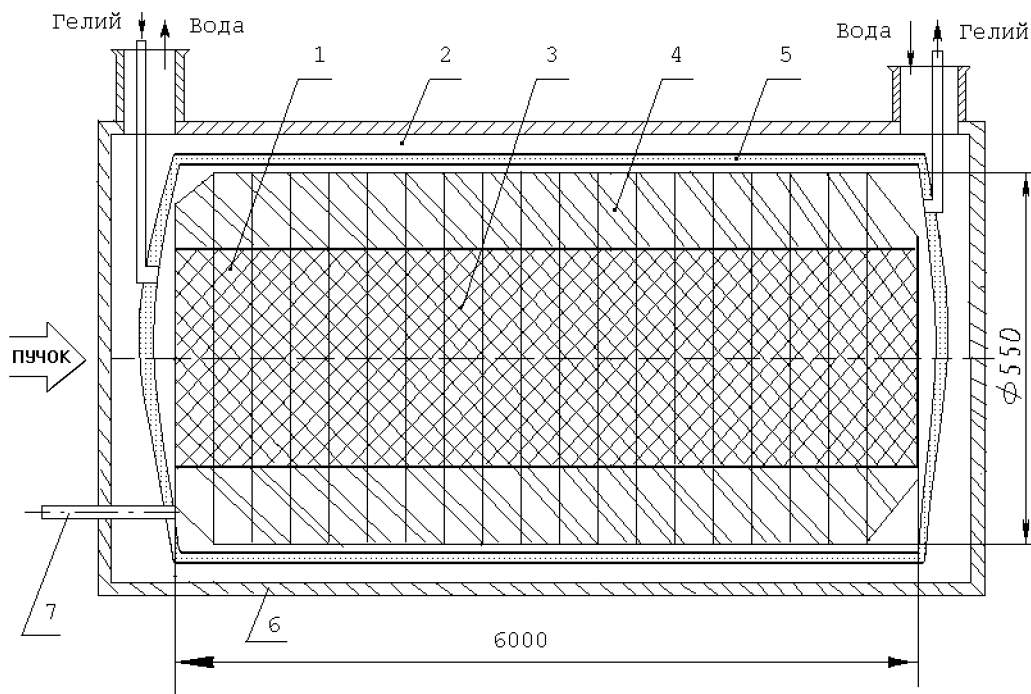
Конструктивная схема поглотителя пучка. 1 — керна; 2 — рубашка охлаждения; 3 — поглощающая секция из графита; 4 — алюминиевый обод поглощающих секций; 5 — стальной корпус керна; 6 — корпус рубашки охлаждения; 7 — вывод трассировки термомпар.
